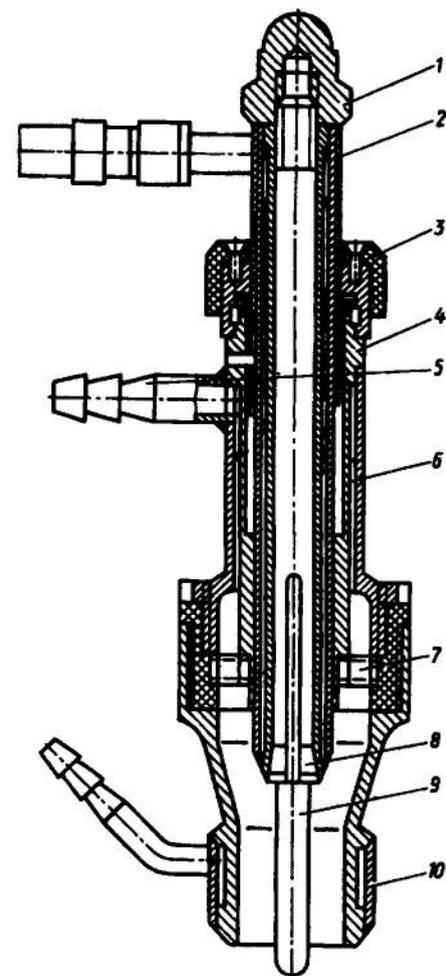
Схема пальника для механізованого зварювання вольфрамовим електродом:
